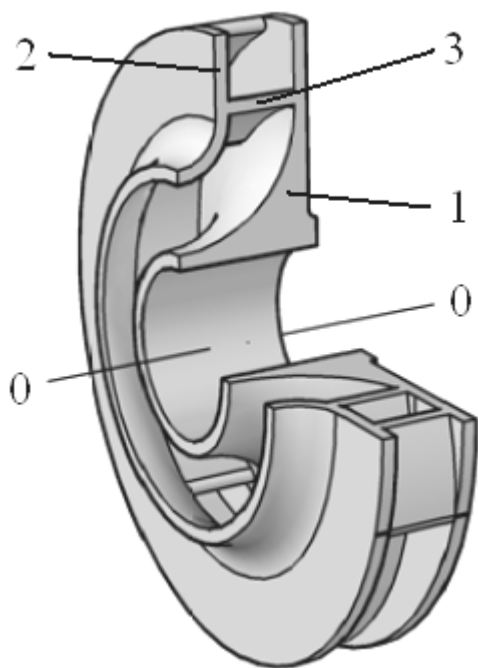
Устройство рабочего колеса центробежного насоса:
